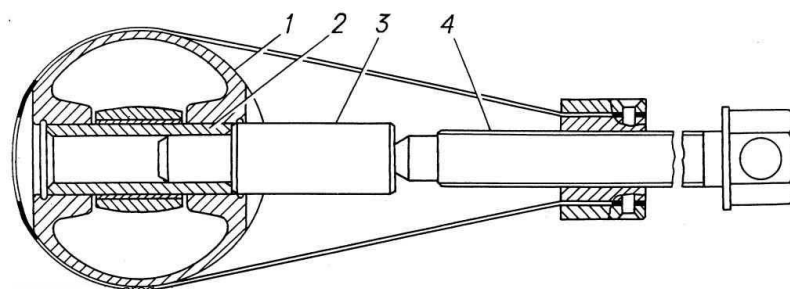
Пристосування для випресовки поршневого пальця: 1 – поршень; 2 – палець; 3 – оправка; 4 – гвинт
